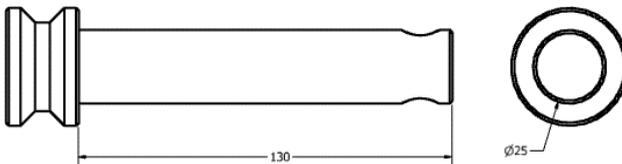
Oberlenkerbolzen komplett Ø25mm.
